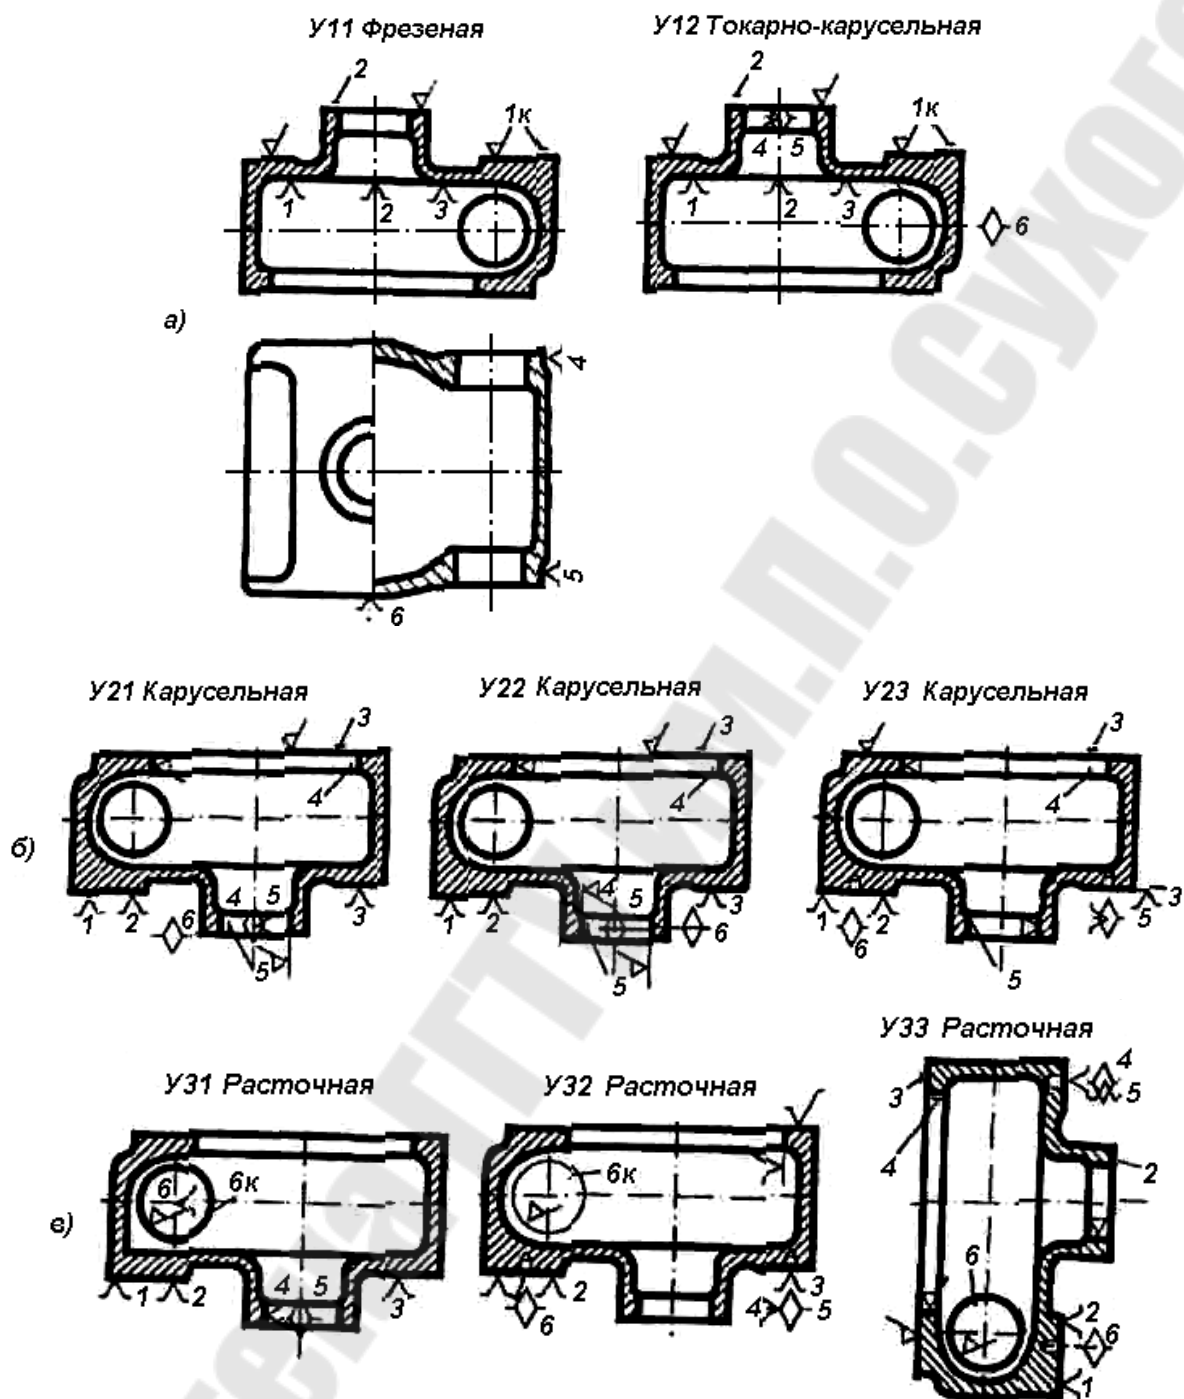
Схемы базирования при обработке поверхностей:
